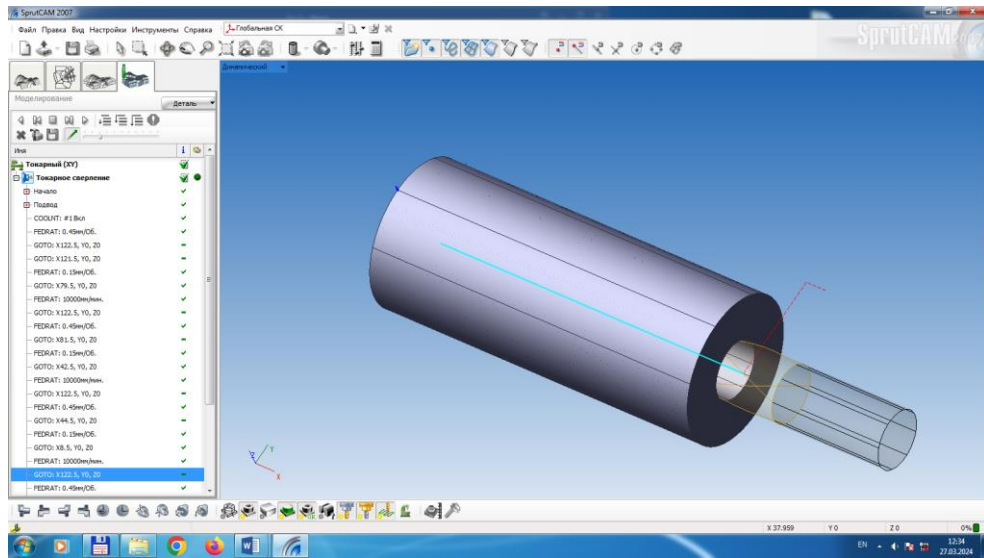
Інструмент і заготовка в процесі обробки
